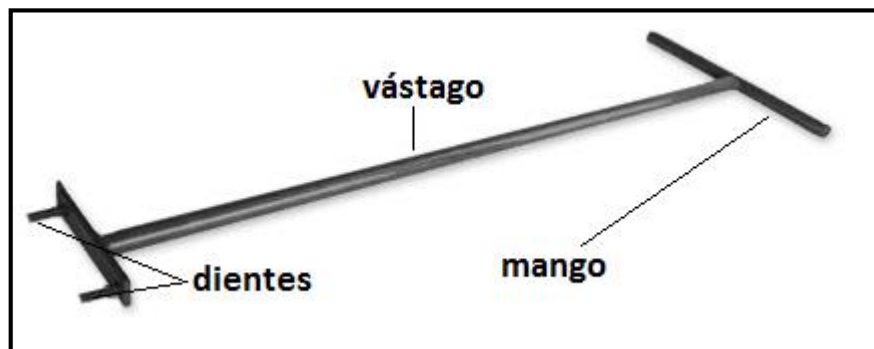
principales partes de una llave de ensamblaje. Fuente: Internet
